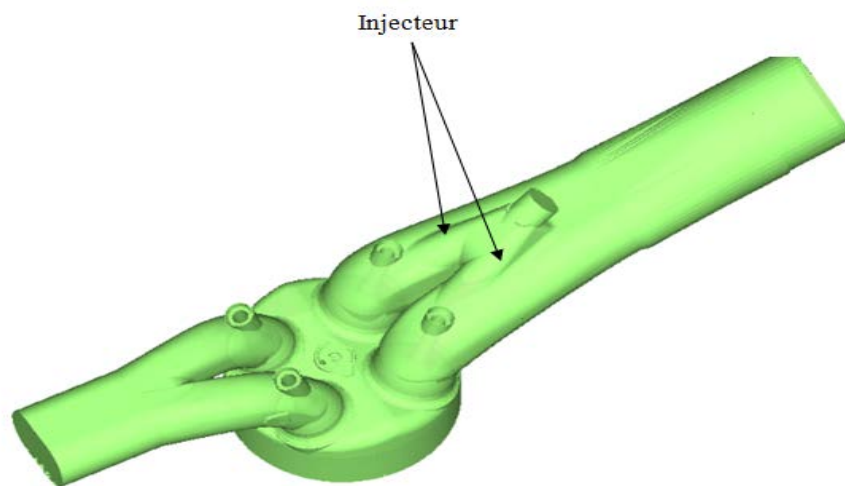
Vue 3D d'un injecteur à 4 becs.
